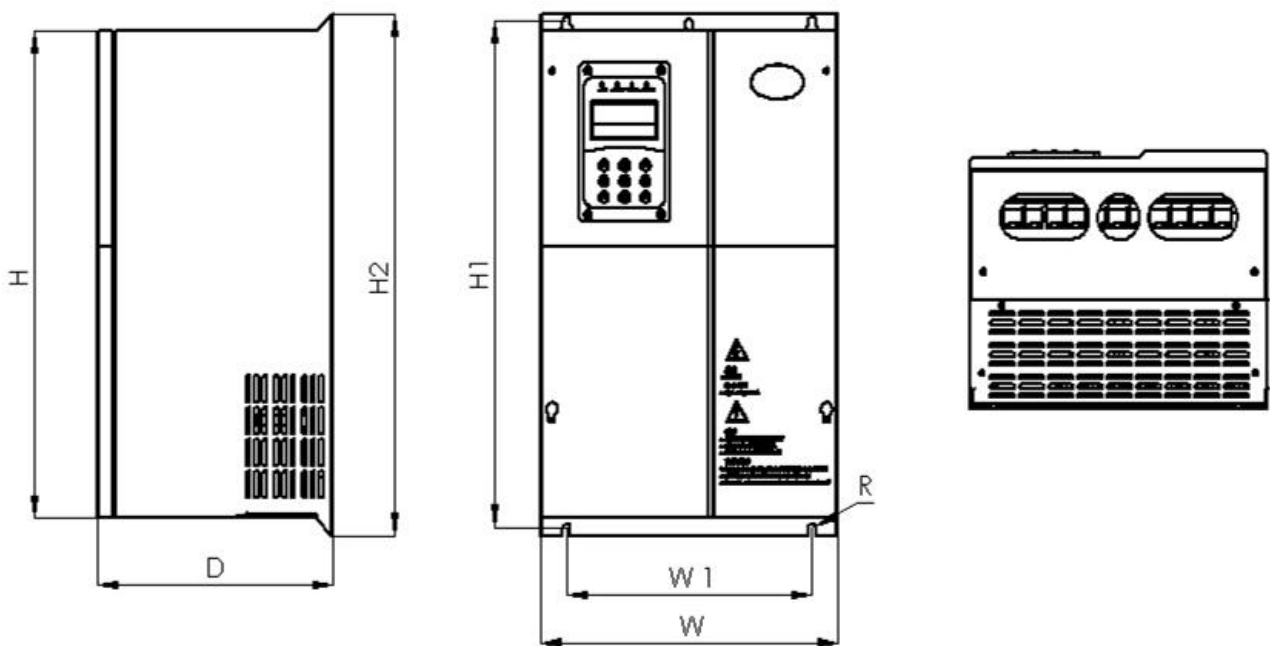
SM22 系列 11-90kW 外型尺寸及安装尺寸示意图
